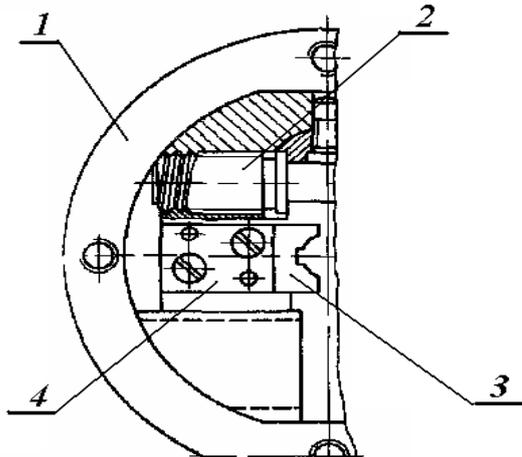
Схема конструкции двухкулачкового самоцентрирующего патрона
